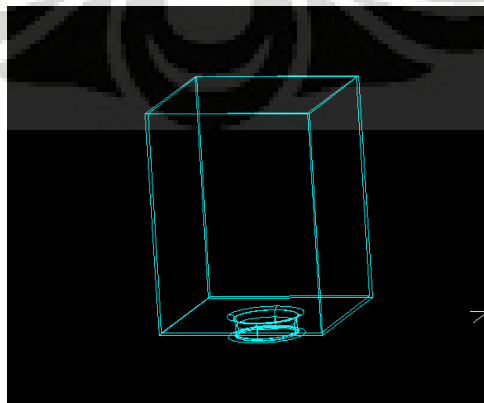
3 Dimensi Desain Gerobak Tampak Depan
